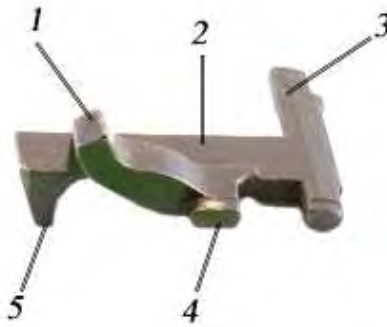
Передаточный рычаг: 1 – верхний выступ; 2 – корпус; 3 – цапфы; 4 – боковой выступ; 5 – нижний выступ
